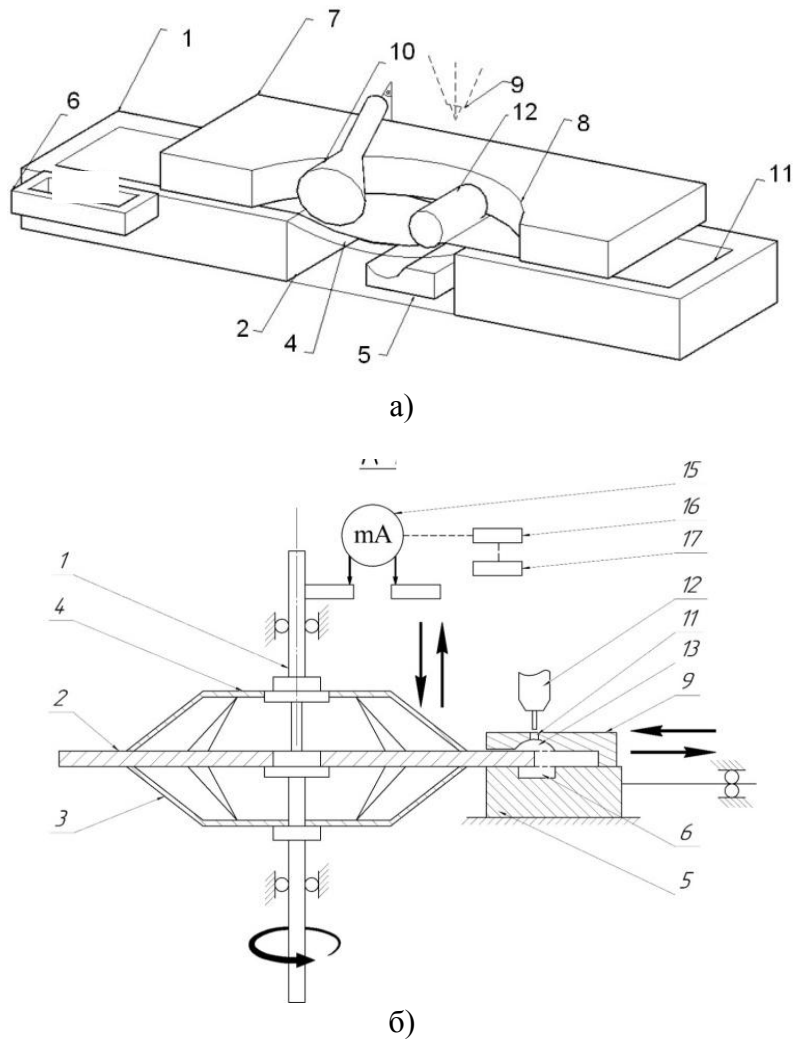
Схеми пристроїв для наплавлення тонкостінних деталей: а) плоскої форми; б) дискової форми
